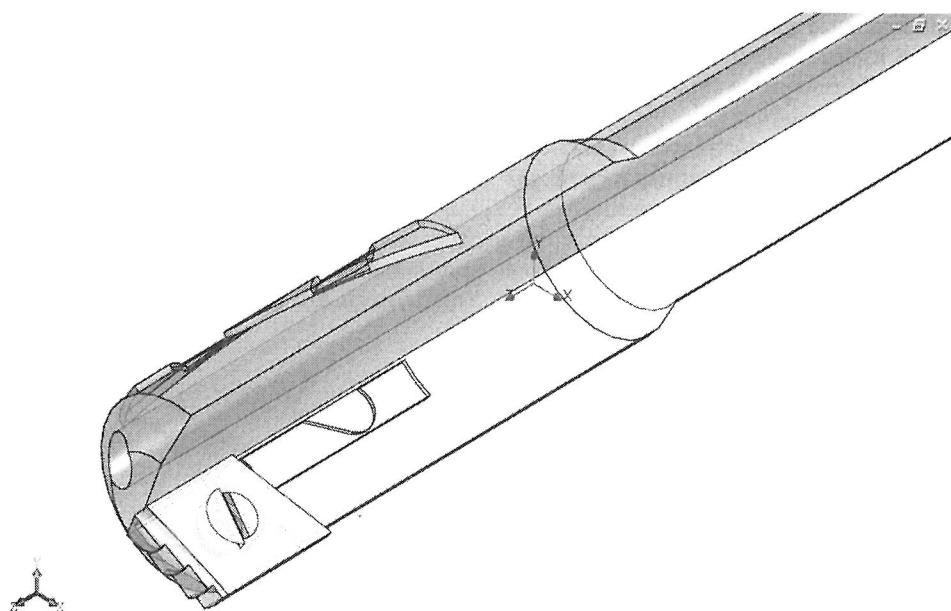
Конструкция сверла со ступенчатой режущей пластиной и дефлектором
